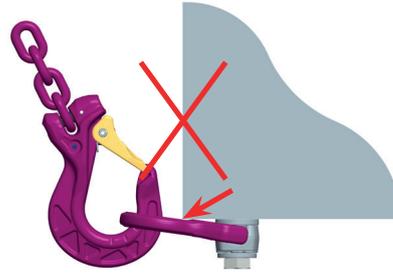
El estribo de carga debe poder moverse libremente y no debe poder apoyarse en bordes o cantos.
